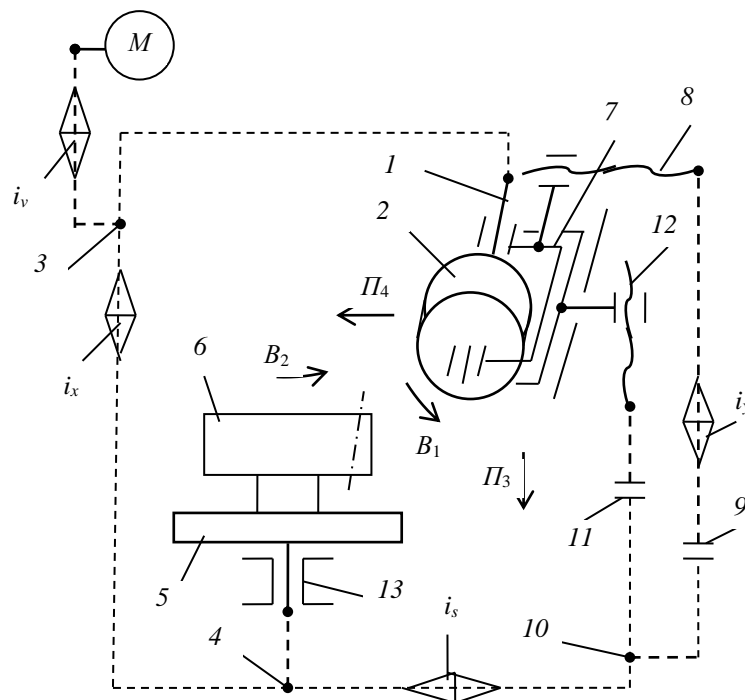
Структурная схема зубофрезерного станка для обработки колес с наклонными зубьями
